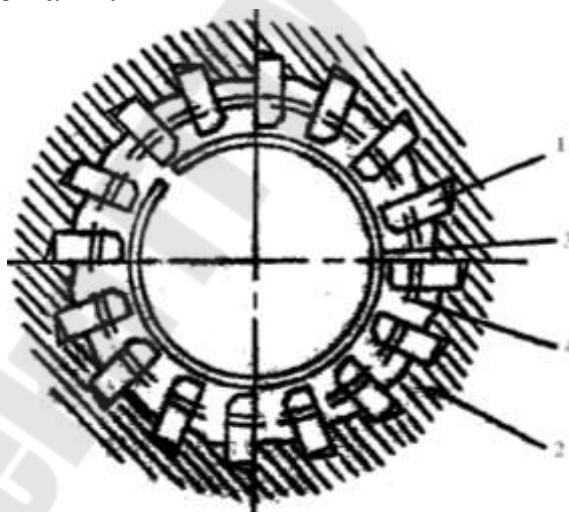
Схема расположения ножей в кокиле: 1 – нож; 2 – кокиль; 3 – стальное пружинящее кольцо; 4 – проволока
